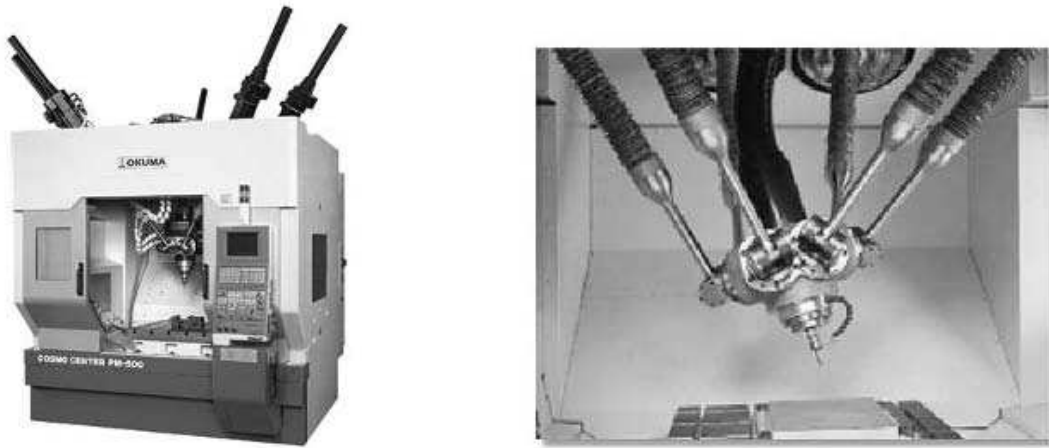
Обрабатывающий центр OKUMA PM-600
